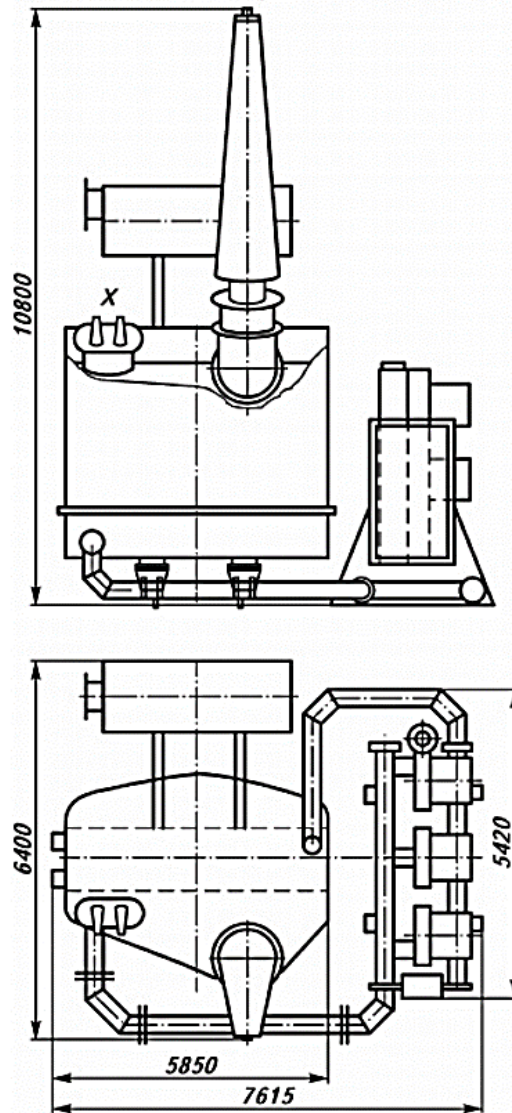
Загальний вигляд та габаритні розміри реактора типу РОДЦ-110 000/750-У1 [65]
